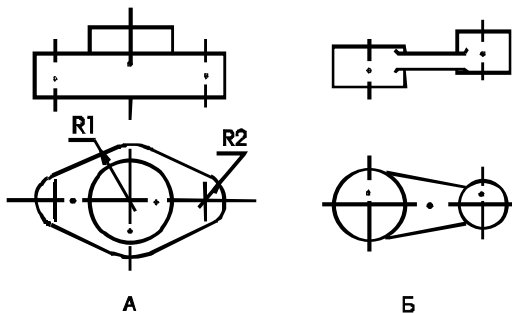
Примеры конструктивных особенностей базирuemых заготовок
